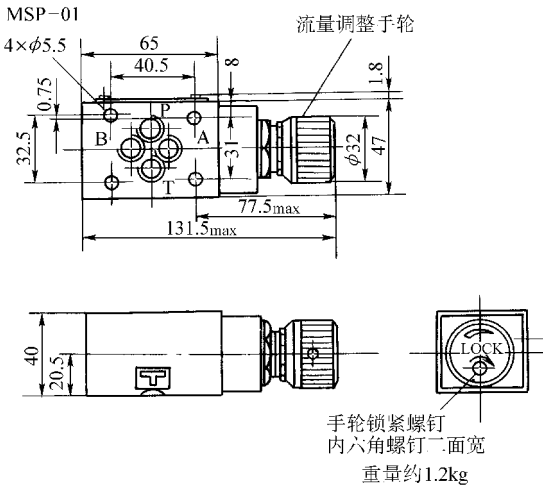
MSP-01 型叠加式节流阀的外形尺寸
